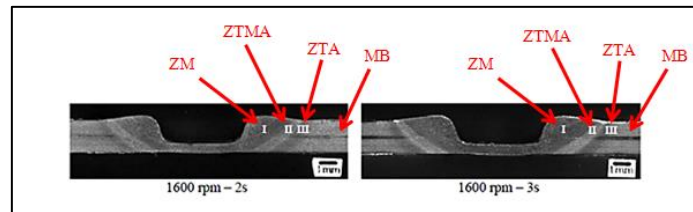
Zonas de uma solda FSSW em aço TRIP 800
